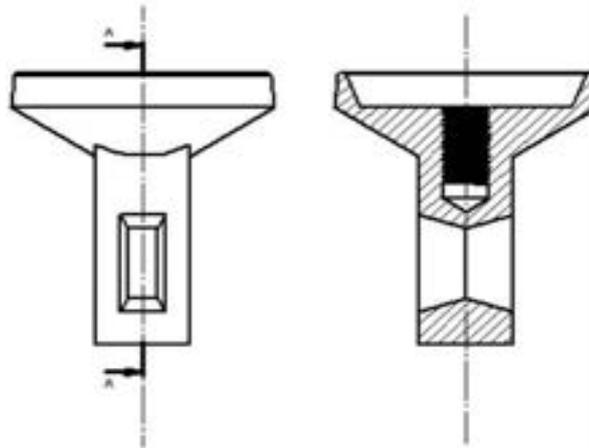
Vista frontal y corte de la pieza que forma parte del obturador del regulador de gas.
